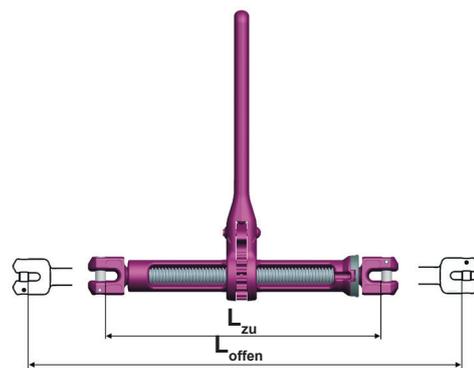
Bemessung ICE-CURT-GAKO Spindelspanner
